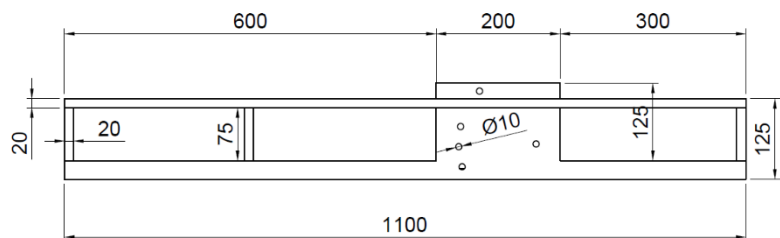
Vista lateral do elemento anelar estrutural e tirante (medidas em milímetros).
